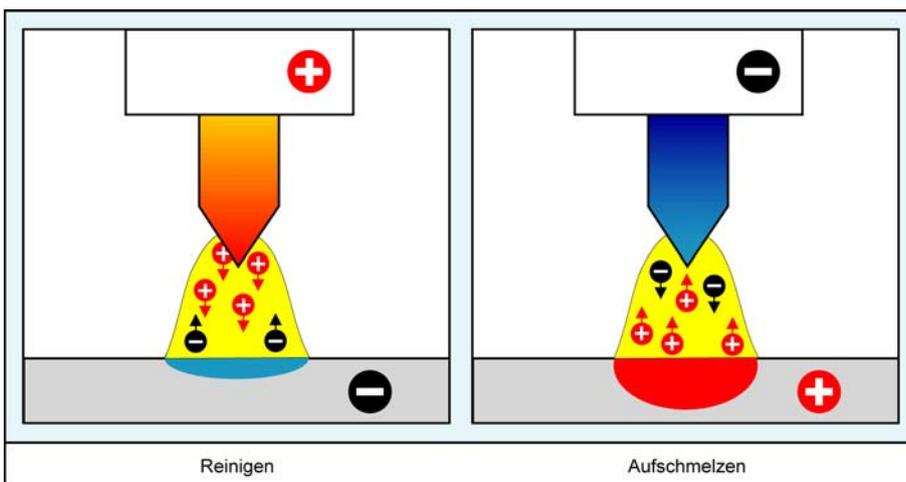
Zum Reinigen der Werkstückoberfläche (Entfernen der Oxidschicht) bei Aluminium wird die Elektrode zuerst gezielt positiv gepolt.
